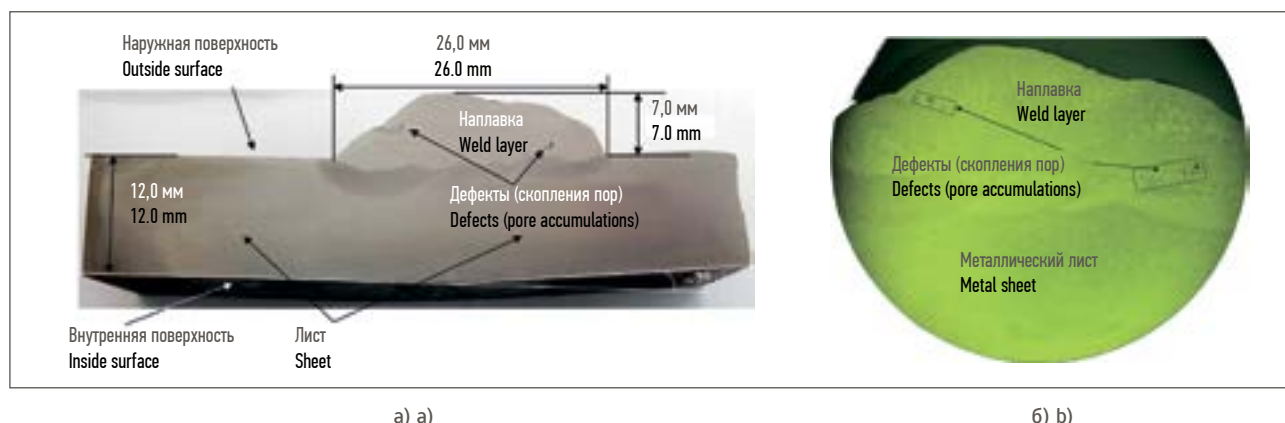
Шлиф образца после РДН: а) общий вид наплавленного слоя; б) скопления пор (фото под микроскопом МБС-10)
